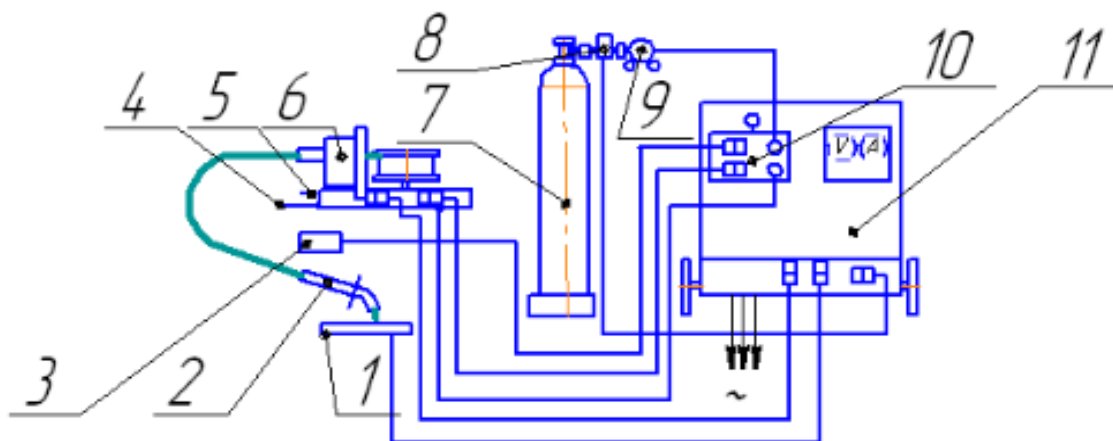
Схема соединений сварочного поста с полуавтоматом ПДГ- 502:
